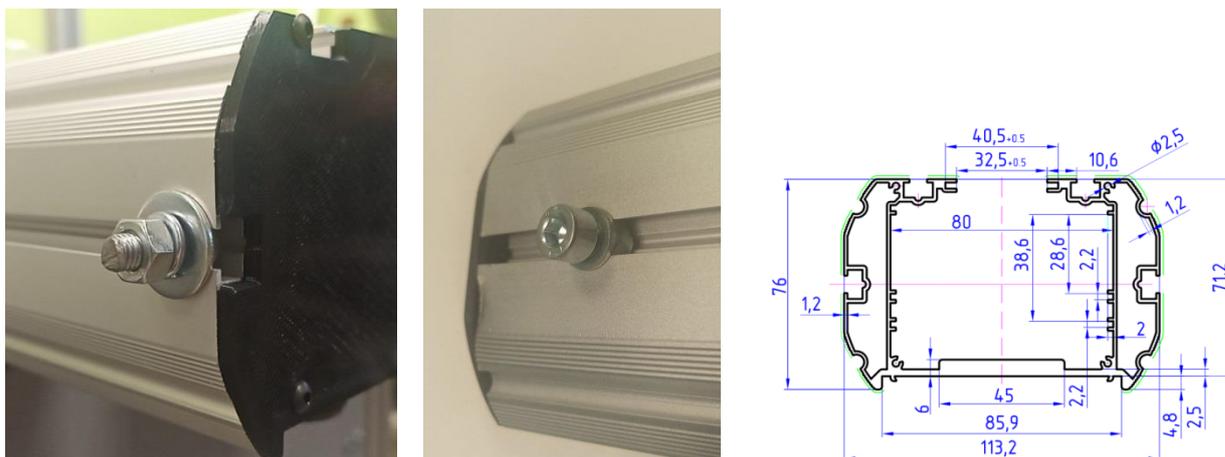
а), б) способы крепления модуля, в) размеры корпуса в сечении
